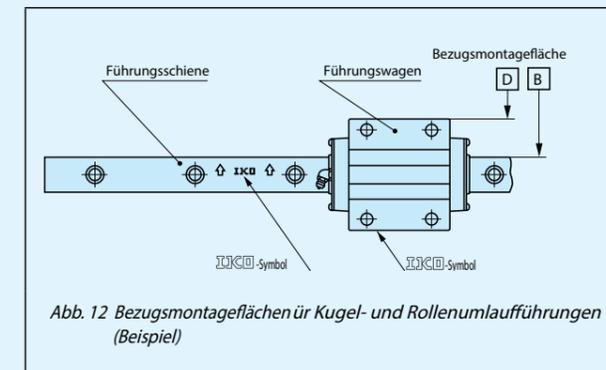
Bezugsmontageflächen für Kugel- und Rollenumlauführungen (Beispiel)
